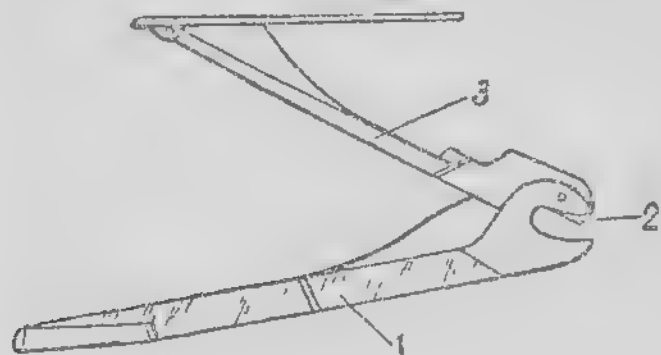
Крышка магазинной коробки с подающим механизмом:
